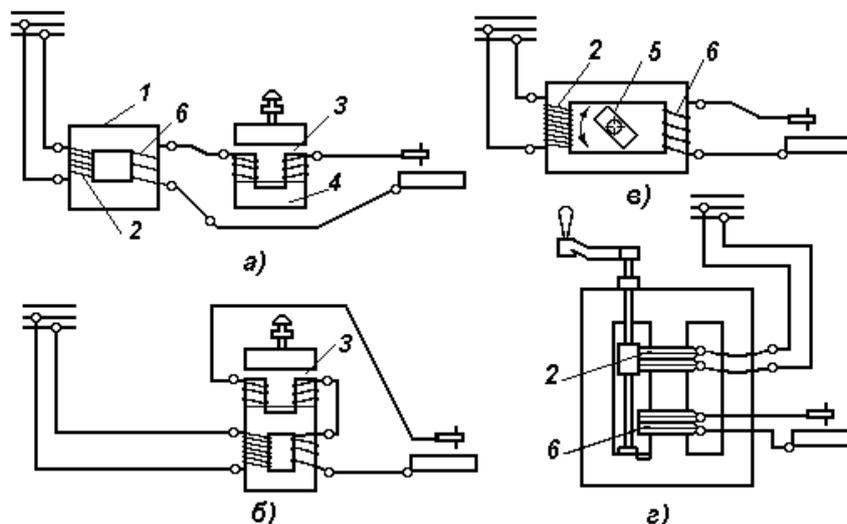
Схемы сварочных трансформаторов:
